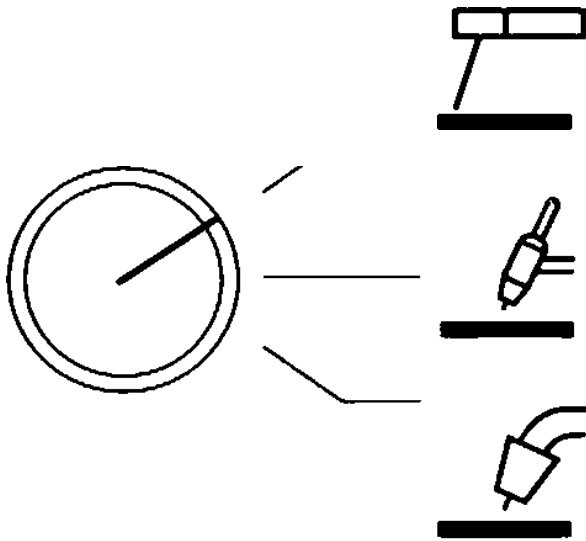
Переключатель процесса сварки РД, РАД, МП (MMA, TIG, MIG)
